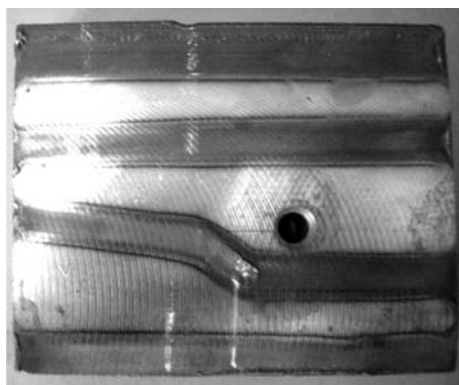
Локальные зоны закалки на поверхности ножа (вид сверху)
